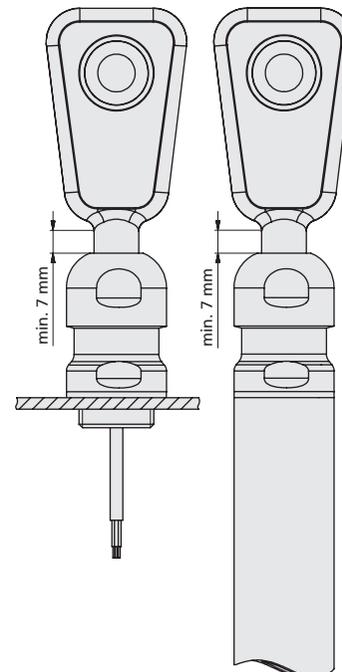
D12-Adapterschaft mit Sensorverschraubung BF-pms/A1 befestigt am Maschinenteil oder am Edelstahlrohr D26,8 mit Innengewinde M20x1,5
